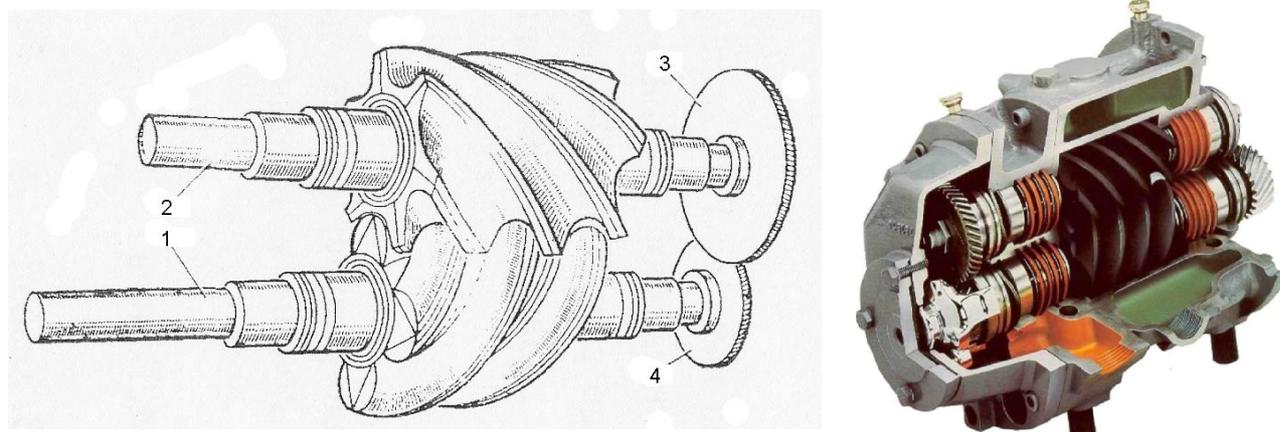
Элементы конструкции винтового пневмомотора:
